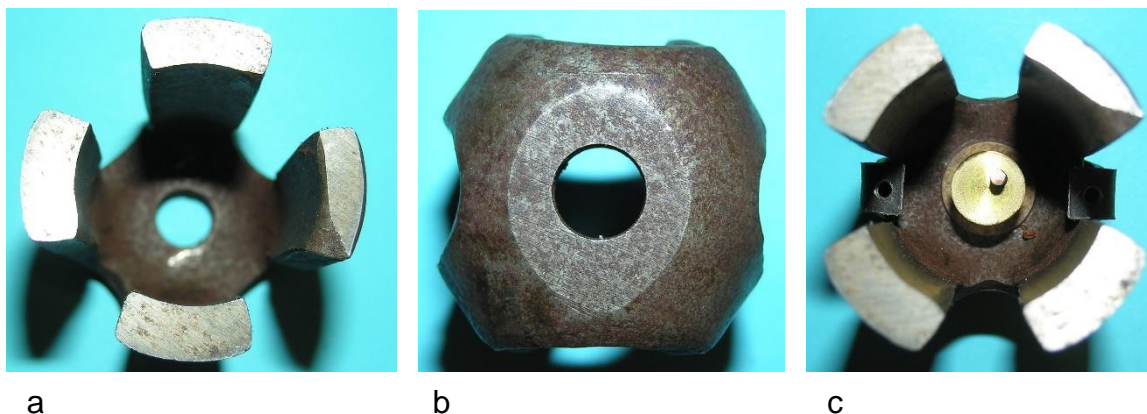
Vierpoliger Tulpenmagnet: Länge 60 mm, Dicke 6,3 mm und 6,9 mm
